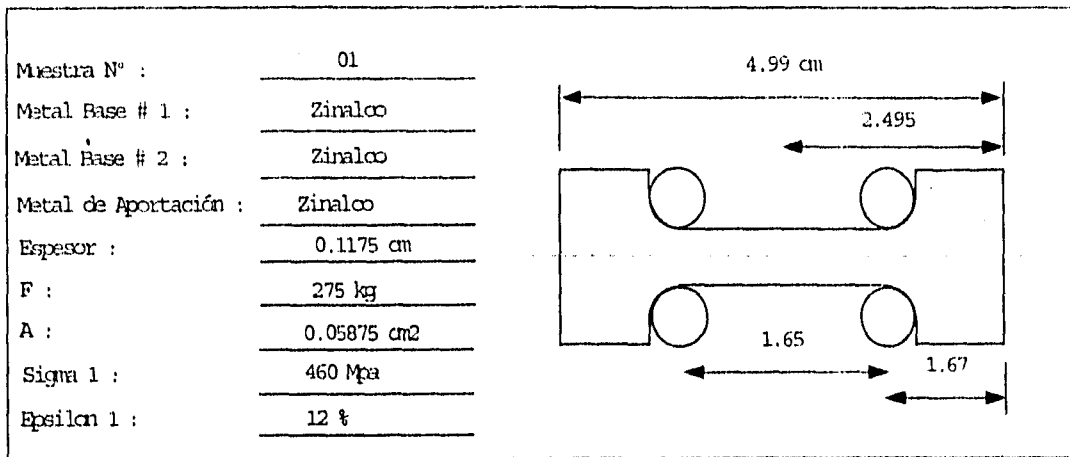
Probeta No.1, valores de prueba a la tensión para soldadura realizada entre Zinalco y Zinalco con material de Aporte Zinalco.
